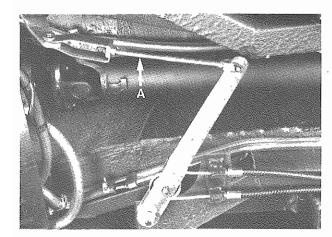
A - Tirante di registro cavi e leveraggi Linkage and cables adjusting rod
